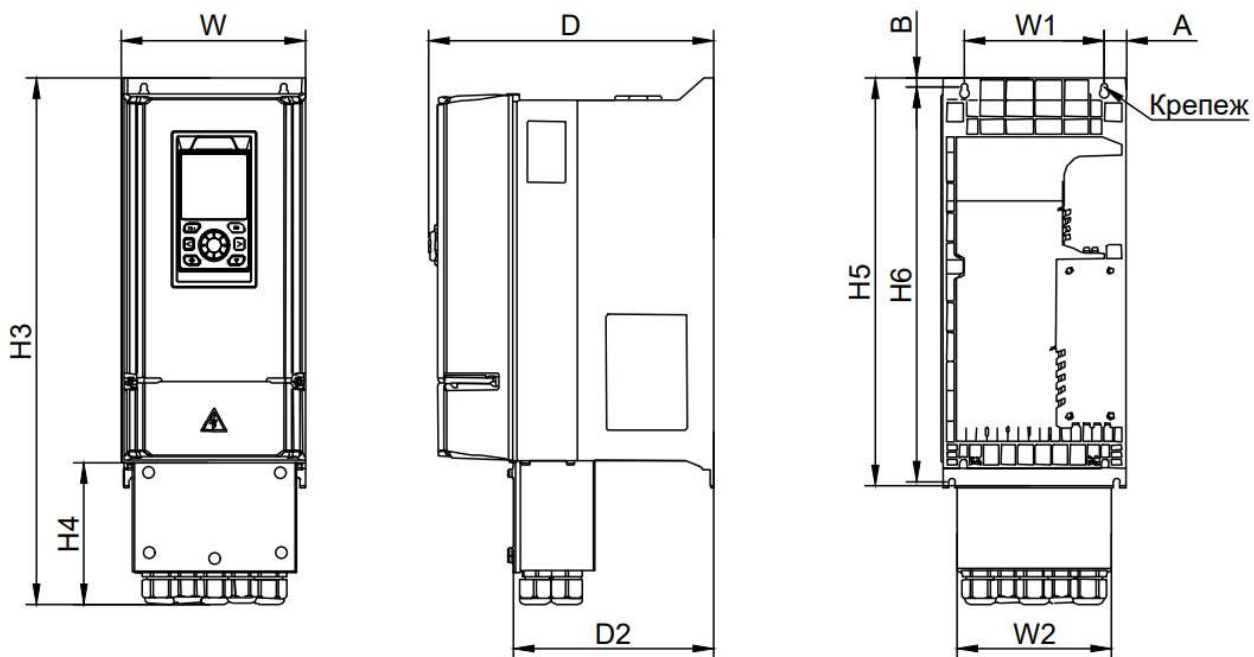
Чертеж преобразователя частоты типоразмеров МН1-МН3
